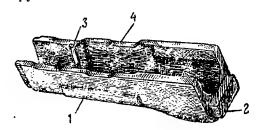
Цевье: 1 — упоры для пальцев; 2 — выступ; 3 → металлическая прокладка; 4 — вырезы
